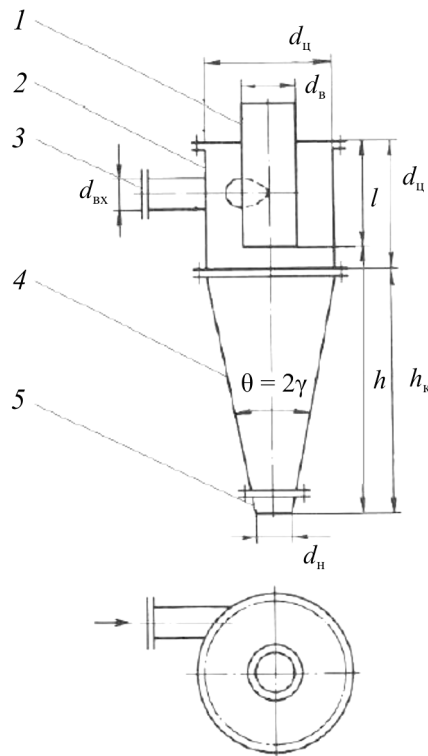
Гидроциклон: 1 – центральный (шламовый) патрубок; 2 – песковая насадка; 3 – камера для слива; 4 – корпус; 5 – резиновый вкладыш
